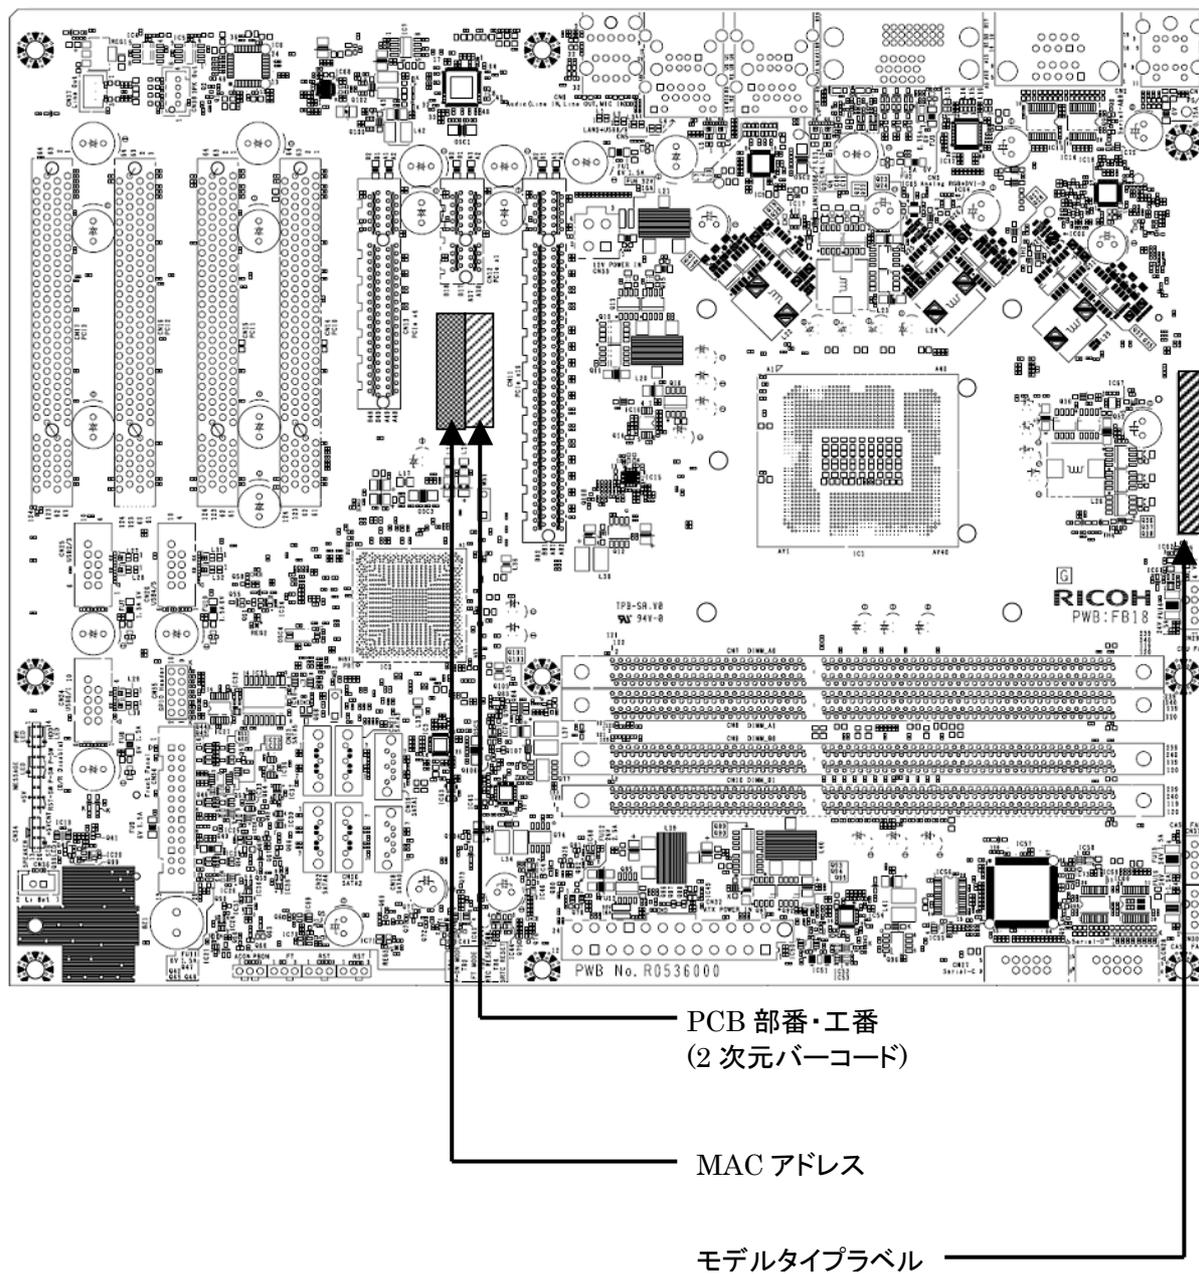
PCB 部番・工番・MAC アドレス・モデルタイプ ラベル配置図
